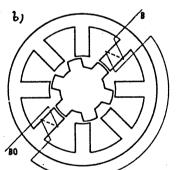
Magnetický obvod krokového motoru s pasívním rotorem
